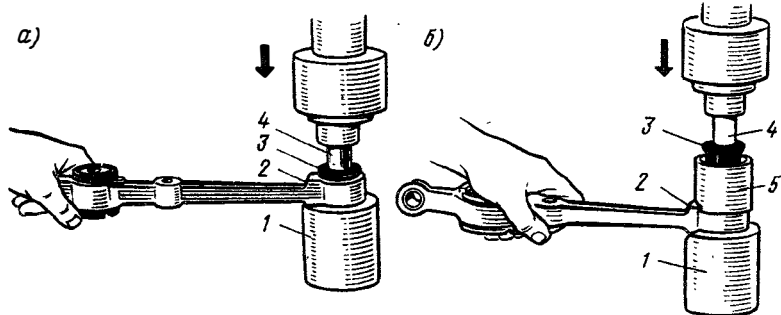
Замена резинометаллического шарнира нижнего рычага передней подвески автомобилей ВАЗ-2108, -2109:
